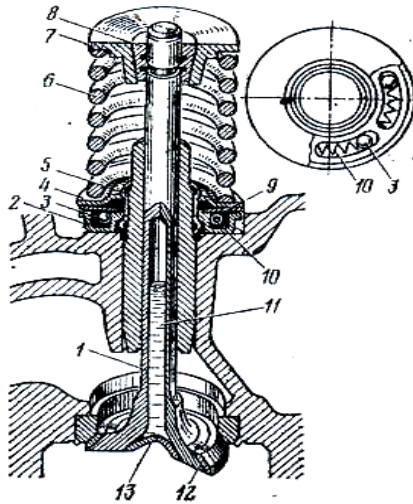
Механізм обертання випускного клапана двигуна ЗІЛ-131
